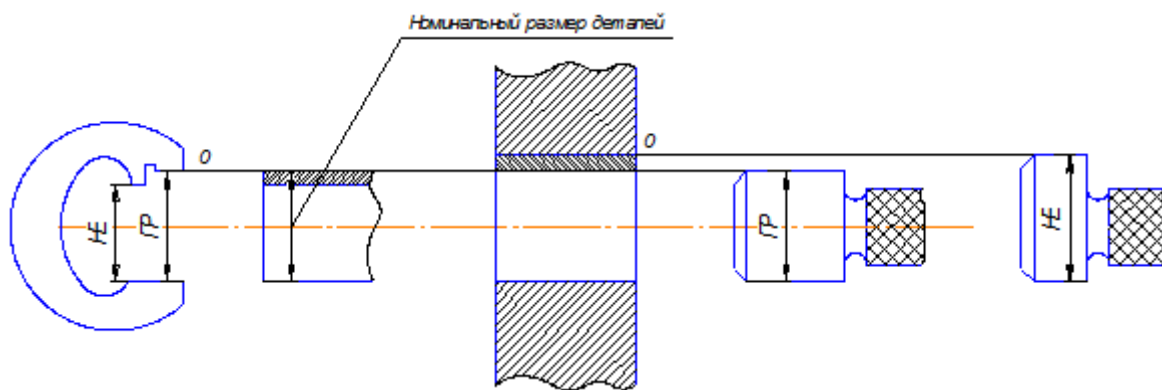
Схема контроля деталей гладкими калибрами
